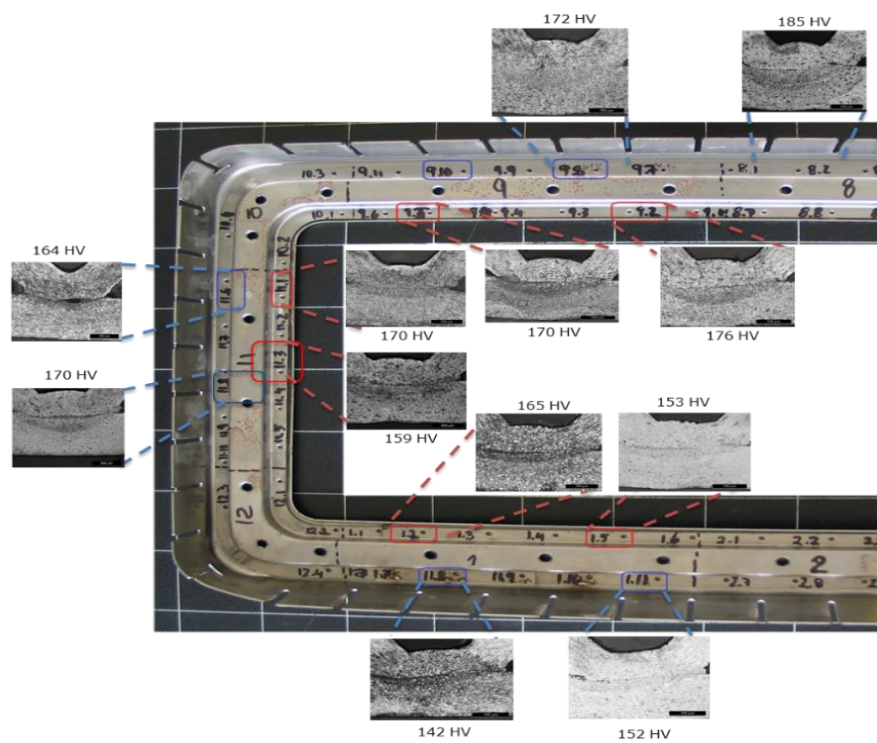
Mapa de soldaduras da peça F37/E26
